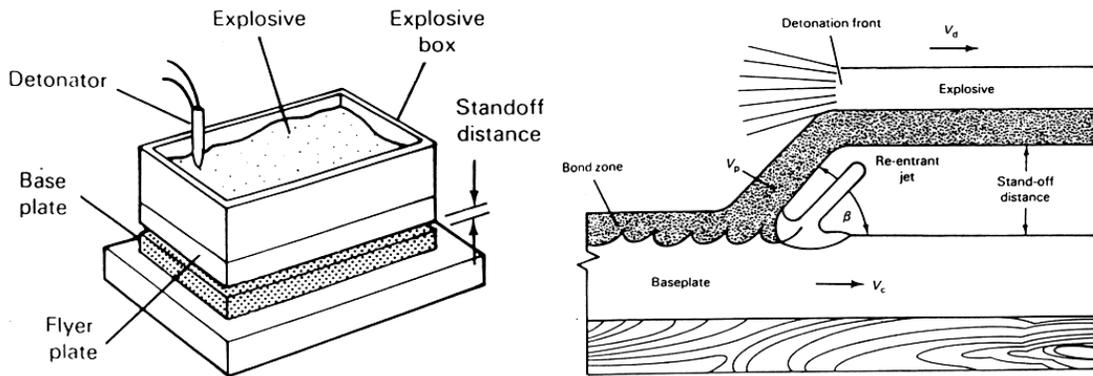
a) schéma de l'arrangement dans le soudage par explosion. L'explosif est placé sur la tôle supérieure qui est posée à une certaine distance de la pièce de base; b) schéma détaillé du point de contact en cas de situation d'équilibre. Le point de contact avance avec la même vitesse que le front de détonation, $V_c = V_d$.
